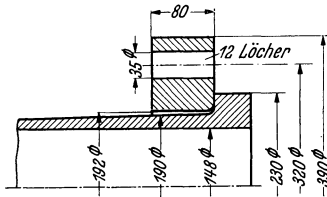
Stauchbund mit loseem Flansch für Höchstdruck-Dampfleitungen.
